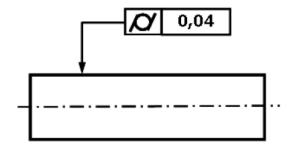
Indicação de Tolerância de Cilindricidade em desenho técnico
